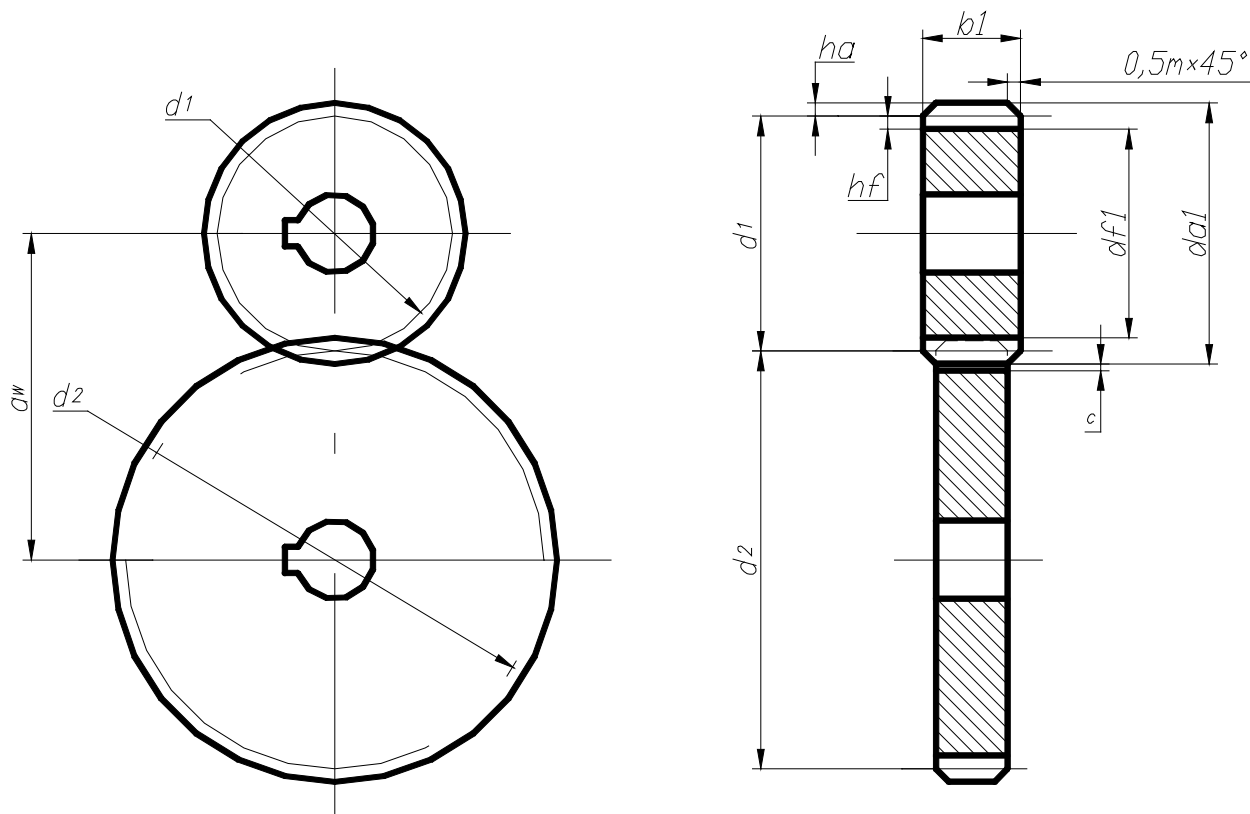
Розрахункова схема зубчатої передачі приводу карусельного вузла розливного автомата
